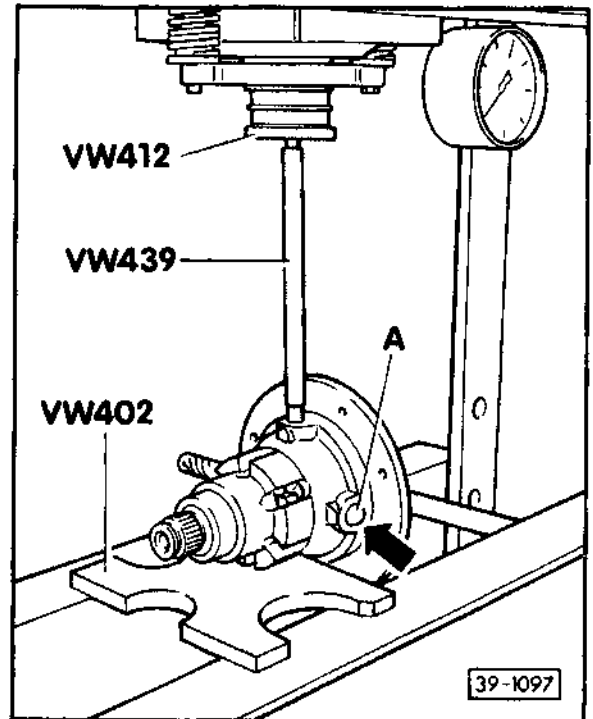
Achsen für Ausgleichkegelräder auspressen
